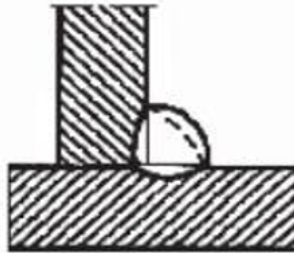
Эскиз дефекта сварного шва
